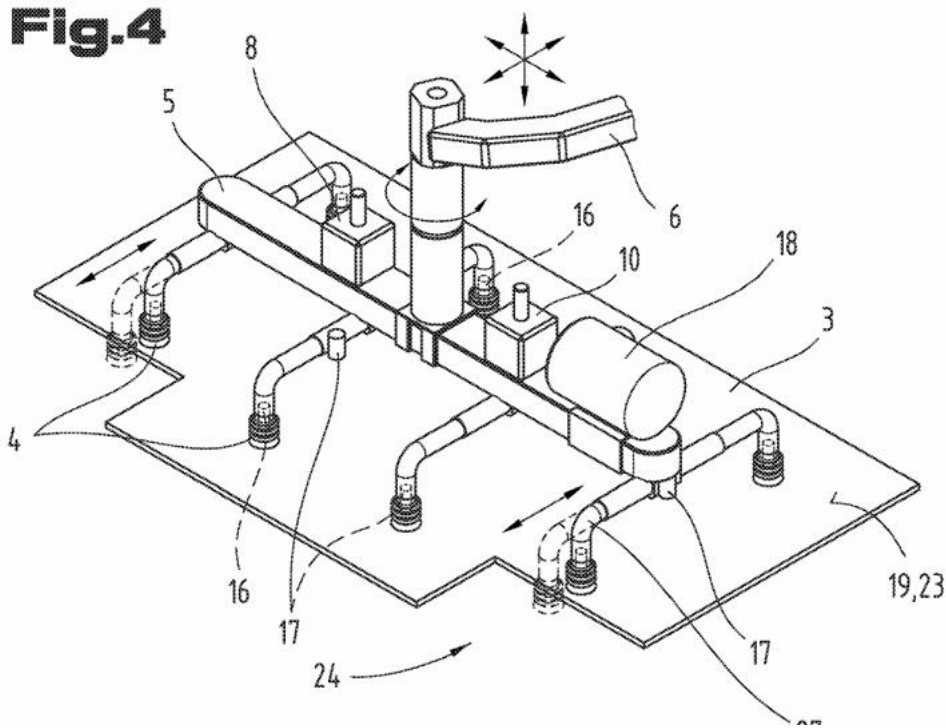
Загальна компоновка та кінематична схема роботизованого модуля сортування готових деталей
